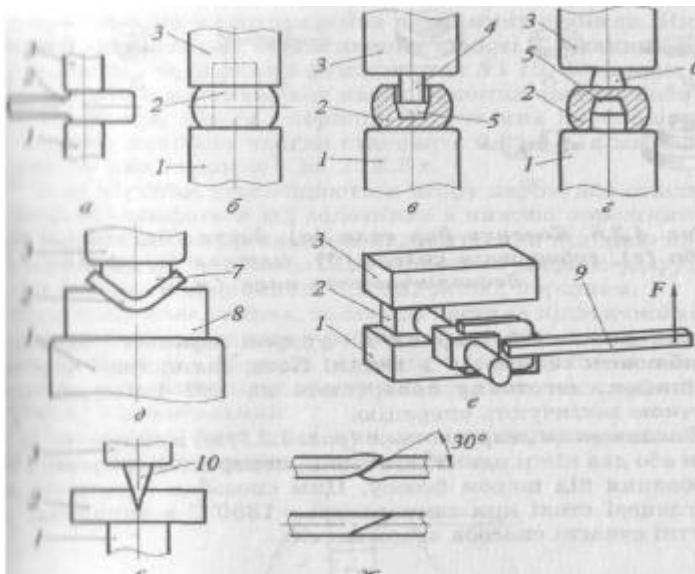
Схеми видовження (а); сплющування (б); пробивання (в,г); гнуття (д); кручення (е); рубання (є) і ковальського зварювання (ж):1-нижній ударник; 2 — заготовка; 3 - верхній ударник; 4 - надставка; 5, 6 - прошивень; 7,8- половини підкладного штампа; 9 - вилка; 10 - сокира; F - сила.
